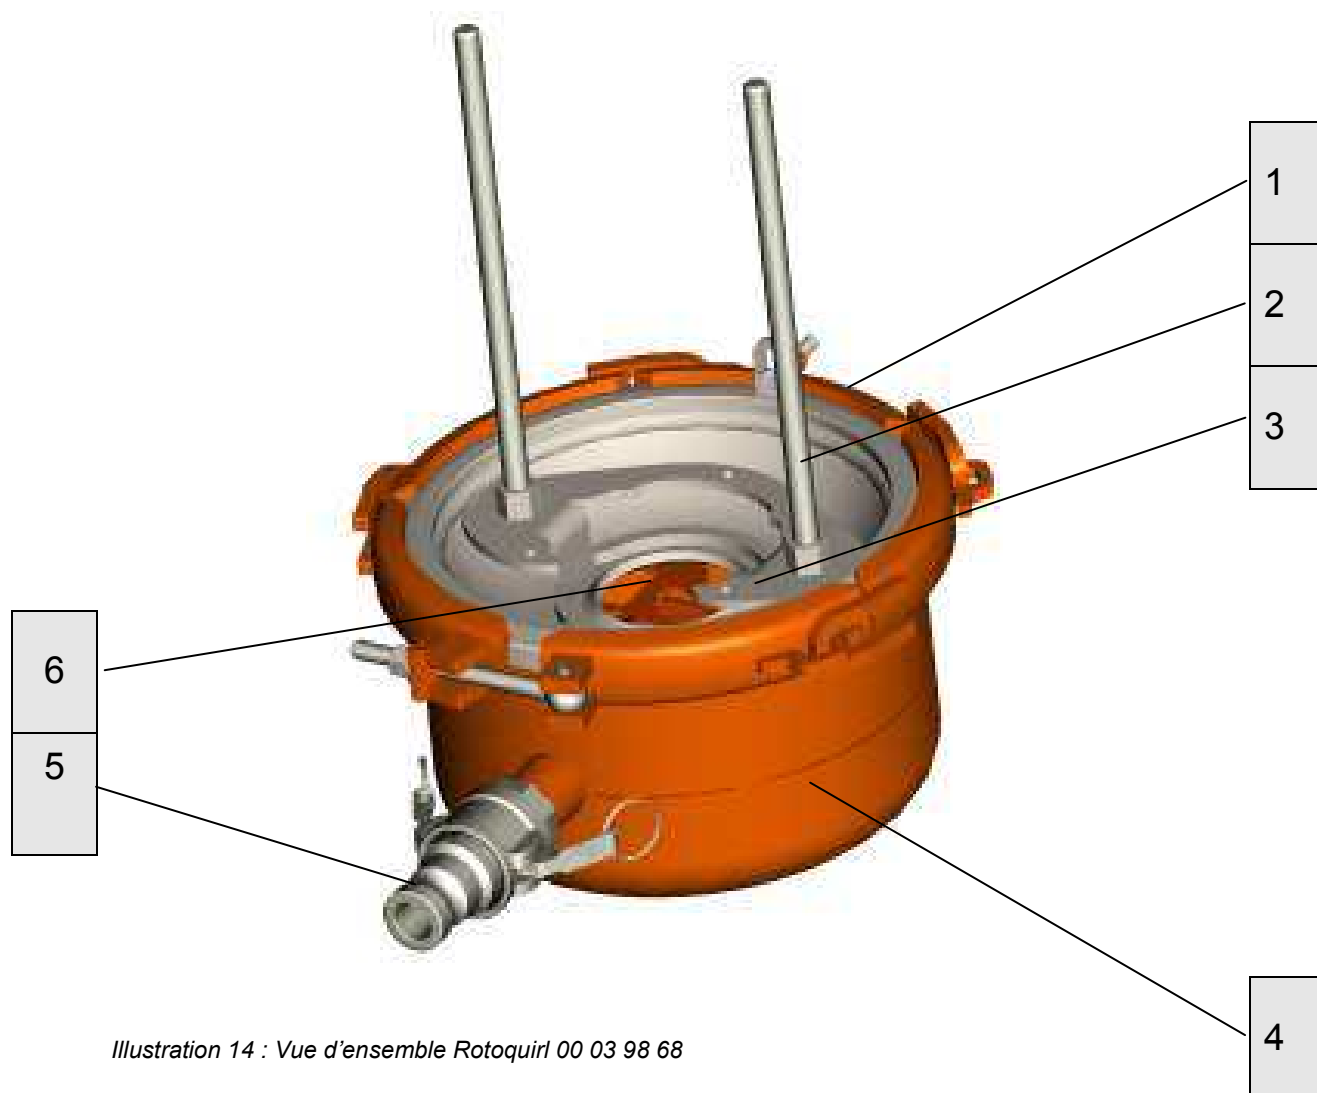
Vue d'ensemble Rotoquir 00 03 98 68
